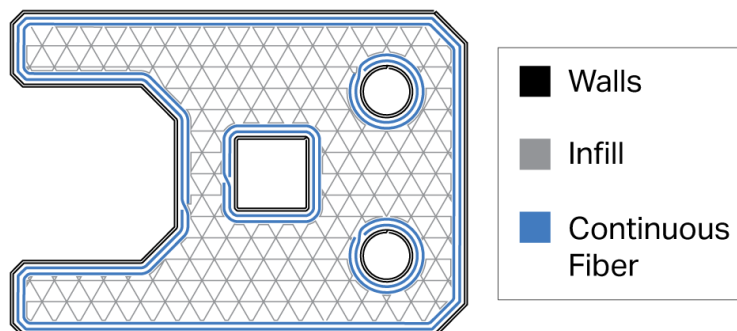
Sección Transversal pieza impresa con CFF
